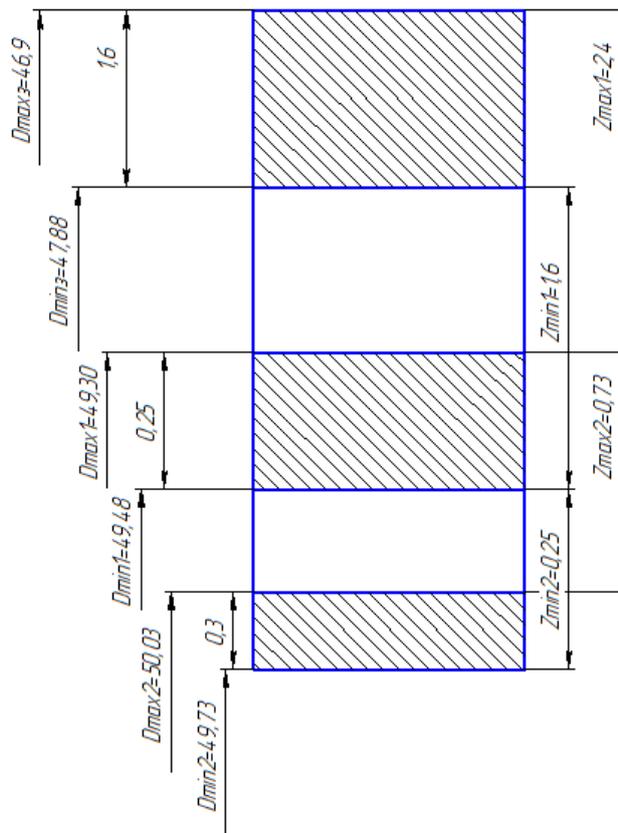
Схема полей допусков и припусков для каждого перехода
